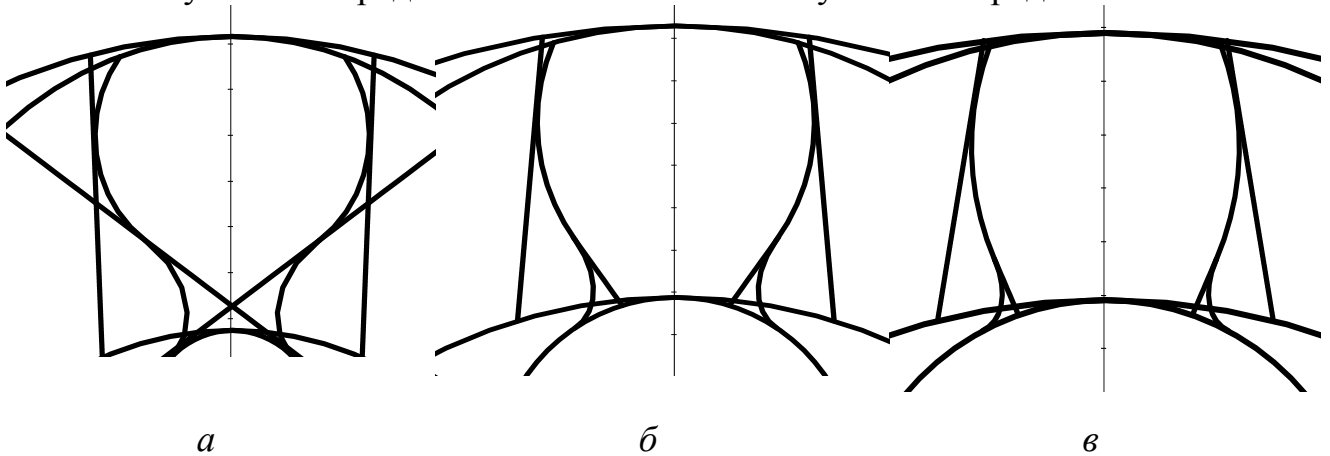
Виды профилей зуба шестерни и впадины колеса при передаточном отношении  $i = 2$  и чисел зубьев:
